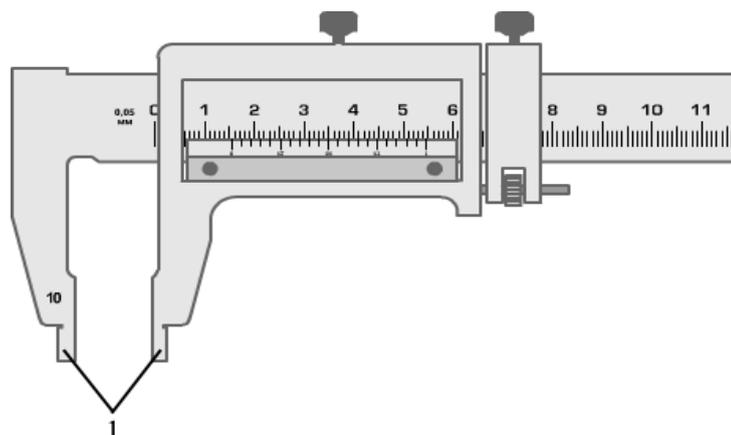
Штангенциркуль ШЦ-ІІІ:1 — губки для зовнішніх і внутрішніх вимірювань
